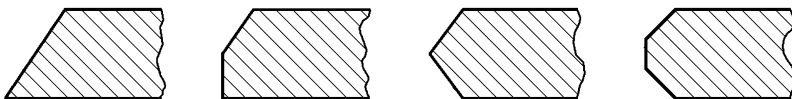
Durchgeschweißte Stumpf- und T-Stöße
